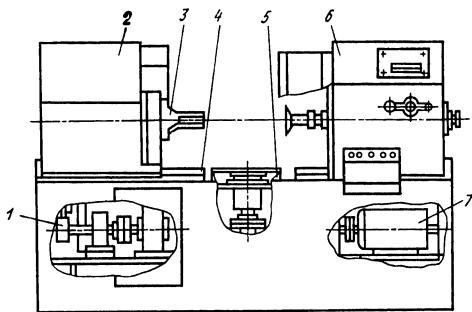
Станок типа СО-3М для обрезки лобовых частей электродвигателей
